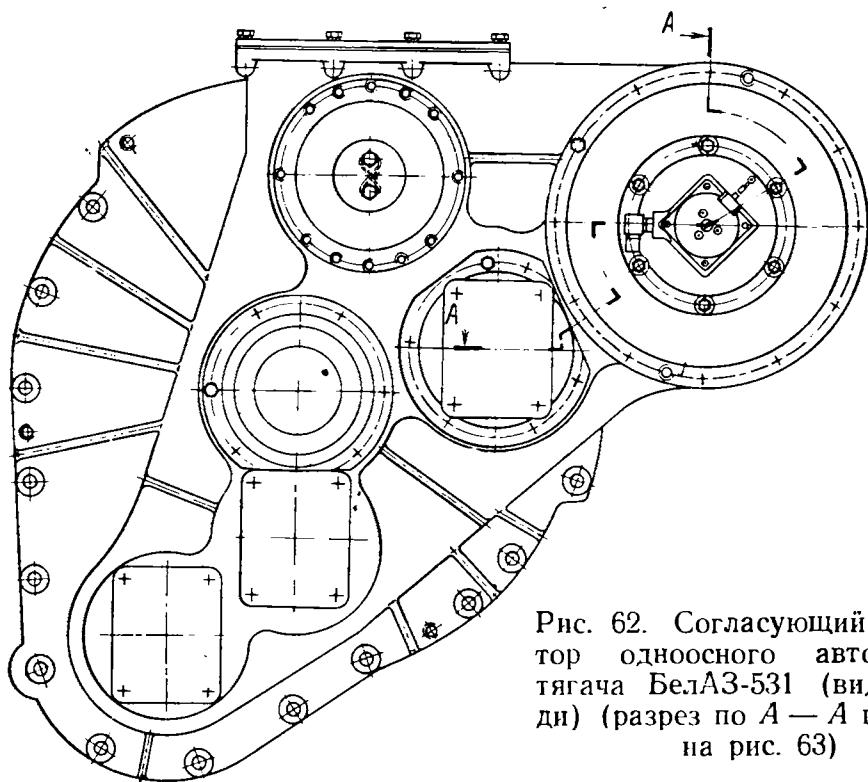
Согласующий редуктор одноосного автомобиля-тягача БелАЗ-531 (вид спереди) (разрез по А — А приведен на рис. 63)
